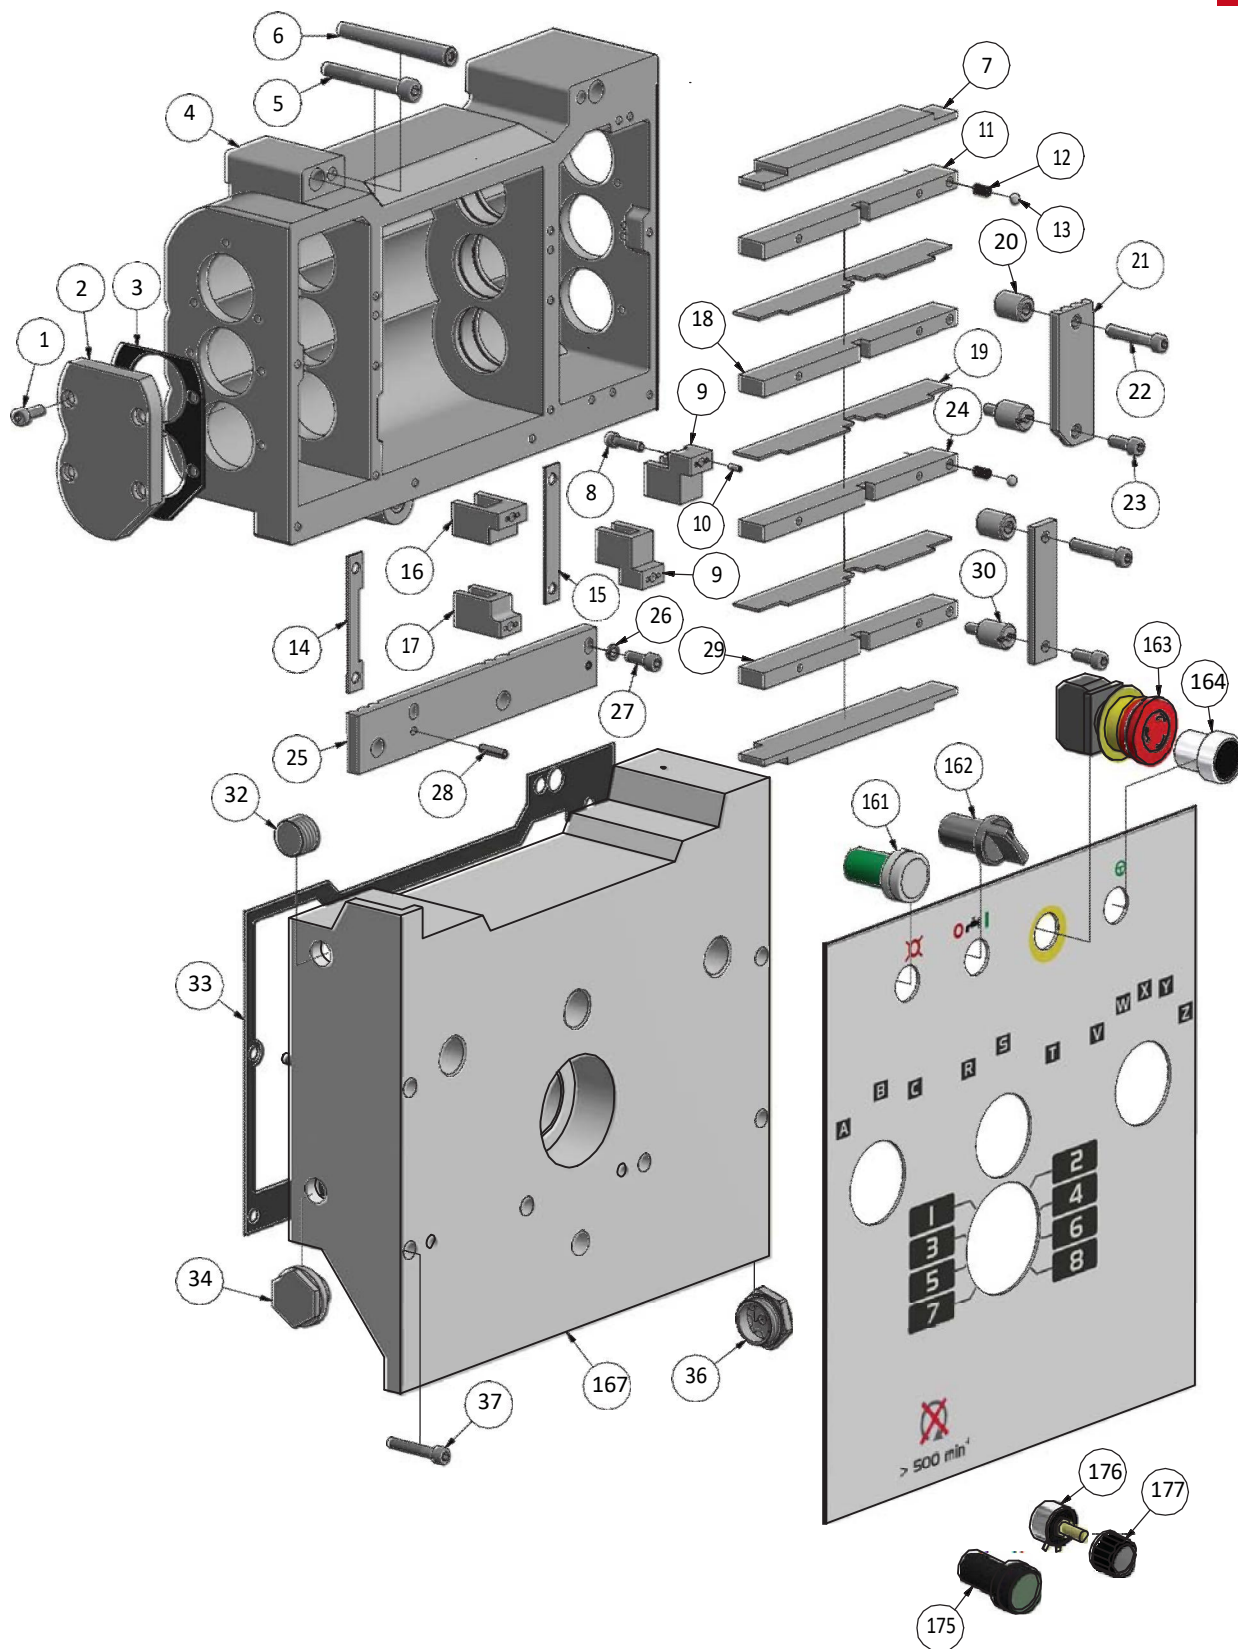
Vorschubgetriebe 2-9 –Engranaje de avance 2-9
